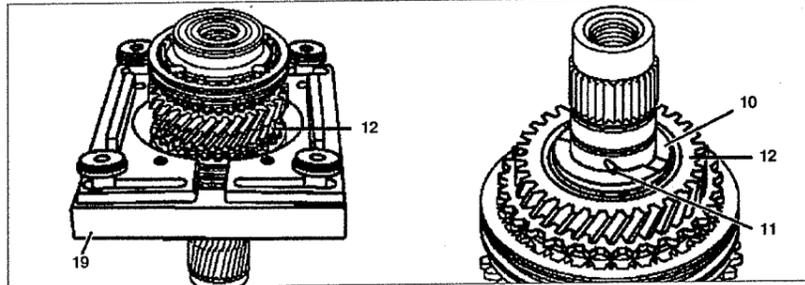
Ведущий вал (автомобили с двигателями 111.948 и 601.970): 10. Упорная прокладка, 11. Шарик, 12. Шестерня 4-й передачи, 19. Съемная плита.
